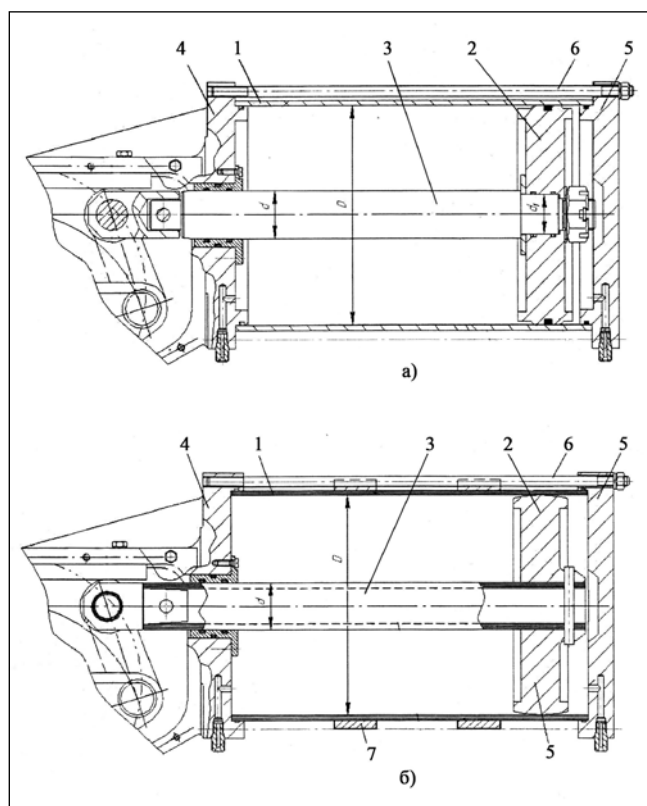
Пневмоцилиндр: а) из трубы, б) навитой из ленты
